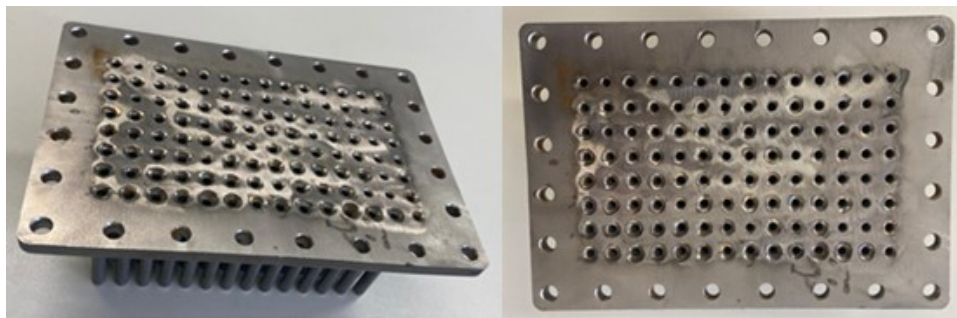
Peça resultante do processo de soldagem dos dutos de saída da seção de testes com a base de solda.
